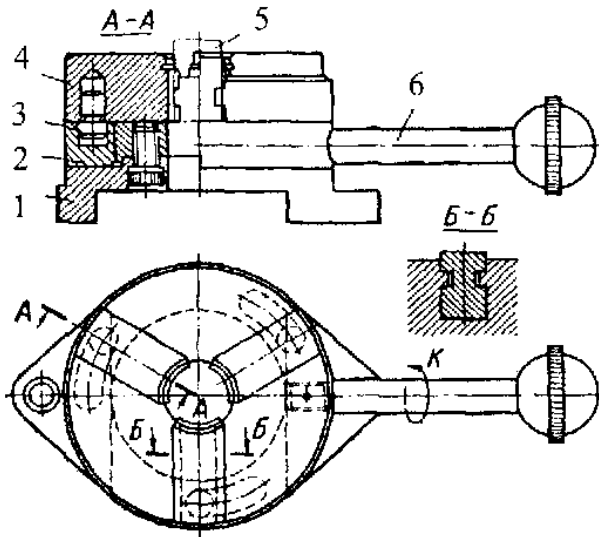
Центруючий механізм з ексцентричними пазами
